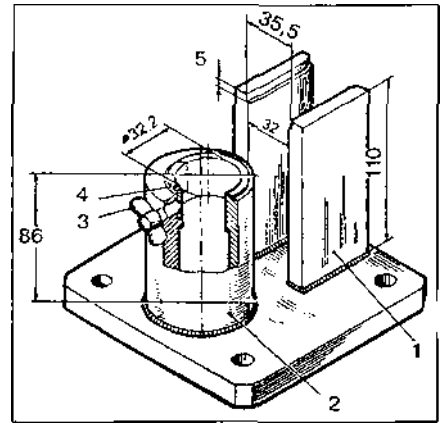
Приспособление М9832-337 для сборки ведомого вала и установки ведущего и ведомого валов:
